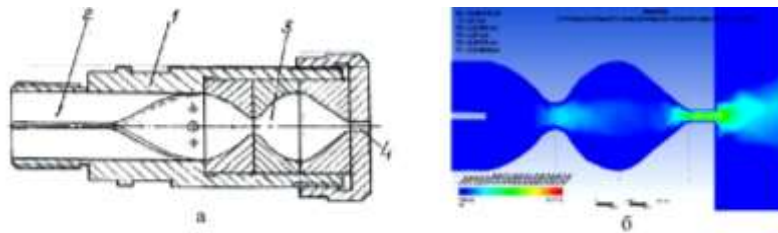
Схема кавітаційної форсунки та розподіл потоку миючої рідини: (а) 1 – корпус; 2 – камера закрутки струменя; 3 – камера Лавалю; 4 – сопло; (б) – оцінка кавітаційного поля миючої рідини з насадка
